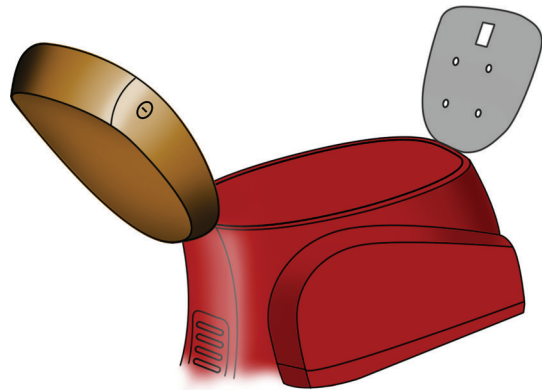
, de plaat klapt eerst dicht en vervolgens het zadel. Door het rechthoekige gat valt de vergrendeling waardoor de onderliggende bak afgesloten wordt.
